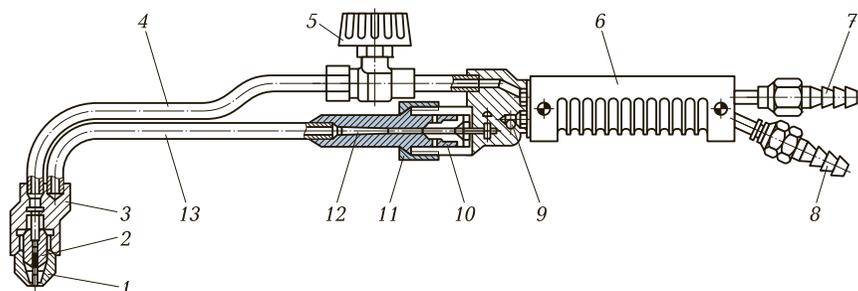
Конструкция ручного универсального резака Р2А-02:
